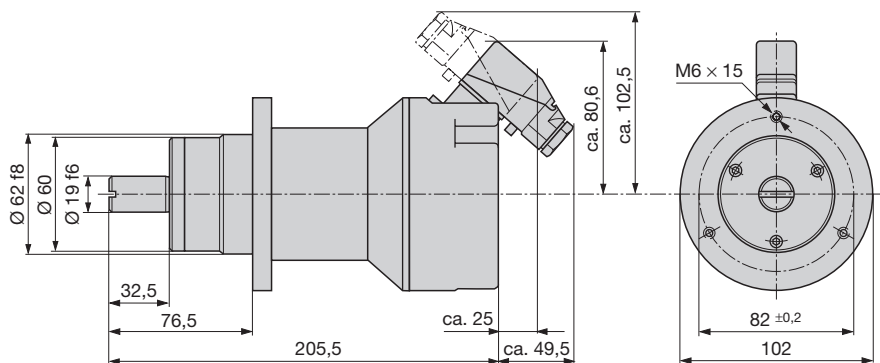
KINAX WT 707 mit Zusatzgetriebe und Steckverbinder.
